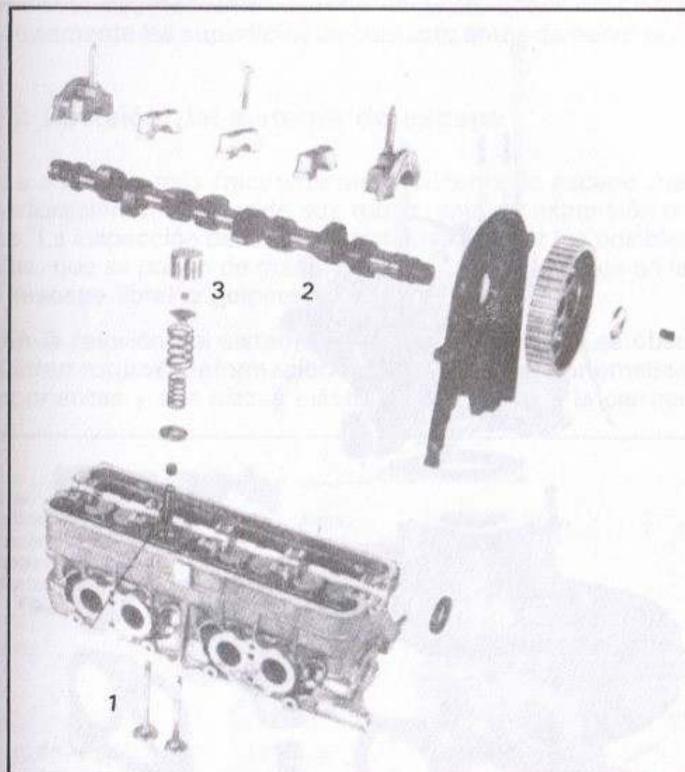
Disposición de montaje y mando de las válvulas.
